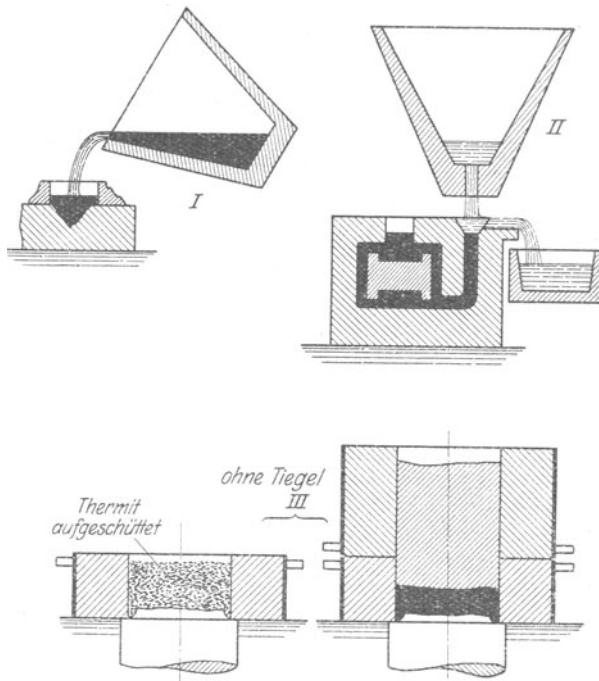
Ausführungsarten der Thermitschweißung.
